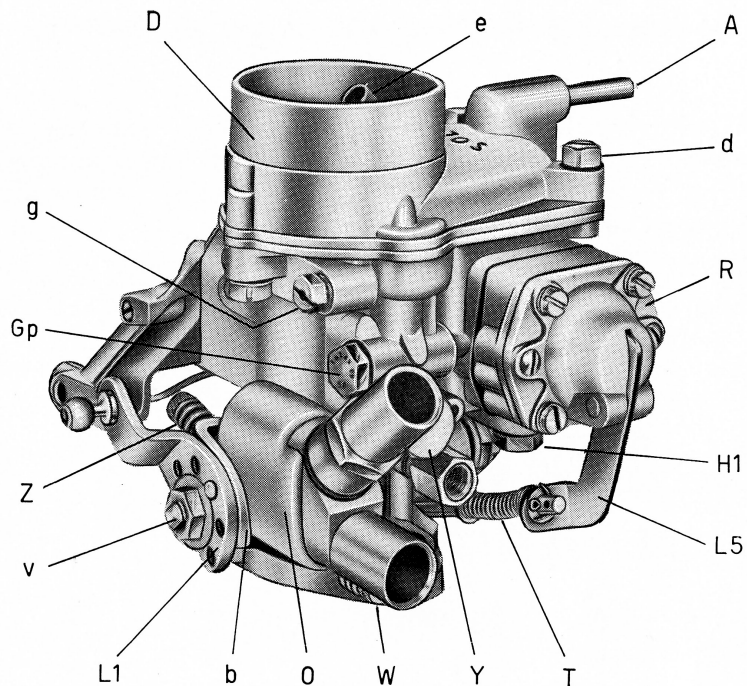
SOLEX-Vergaser Type 32 PICBA — Ansicht
